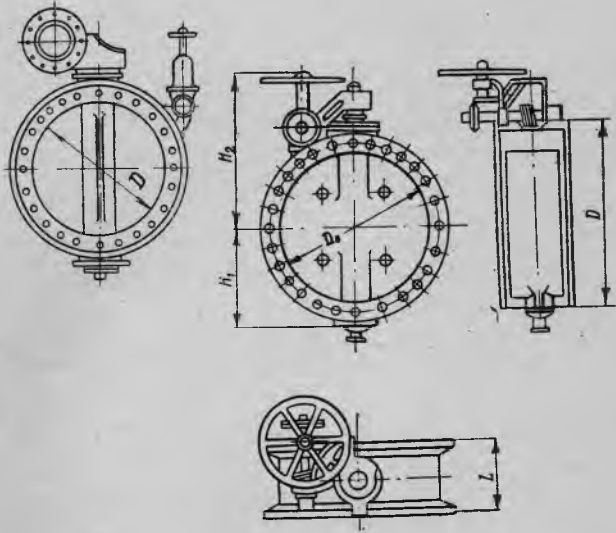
Поворотный дисковый затвор с ручным приводом.
